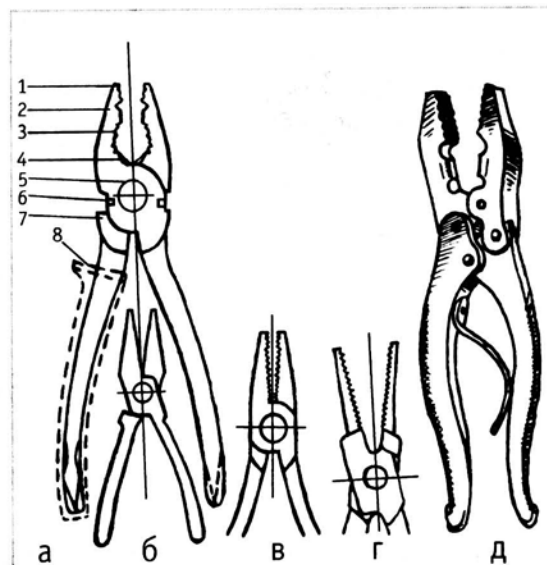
Плоскогубцы: а — комбинированные: 1 — плоский участок с прямой или крестообразной насечкой; 2 — губка; 3 — дугообразный участок с зубцами для зажима цилиндрических деталей; 4 — режущие кромки или лезвия; 5 — ось; 6 — прорезы для откусывания круглой проволоки; 7 — ограничитель разворота рукояток; 8 — диэлектрические чехлы; б — узкогубцы; в — простые или обыкновенные; г — круглогубцы; д — шарнирные
